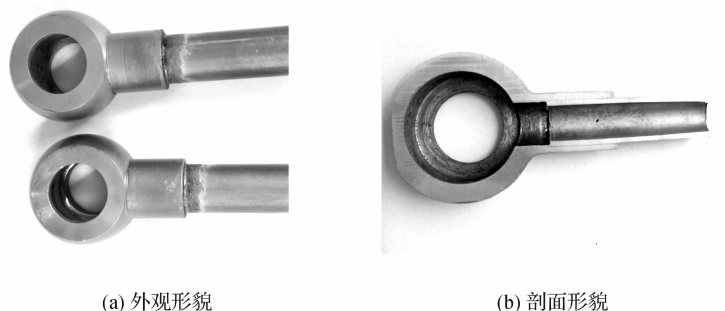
邦迪管钎焊接头焊缝的形貌
